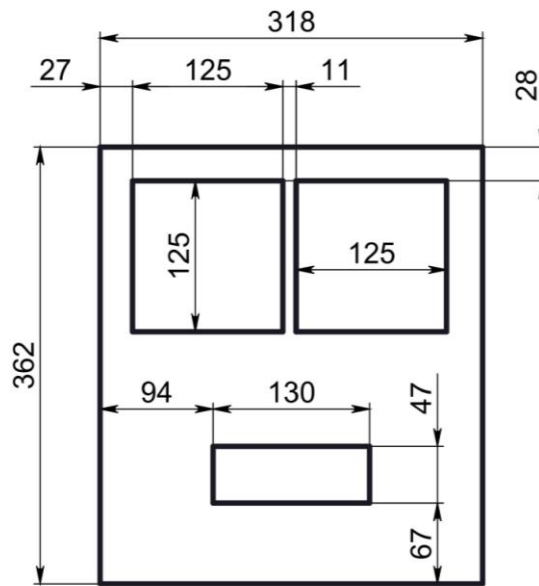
Габаритные, установочные и присоединительные размеры
